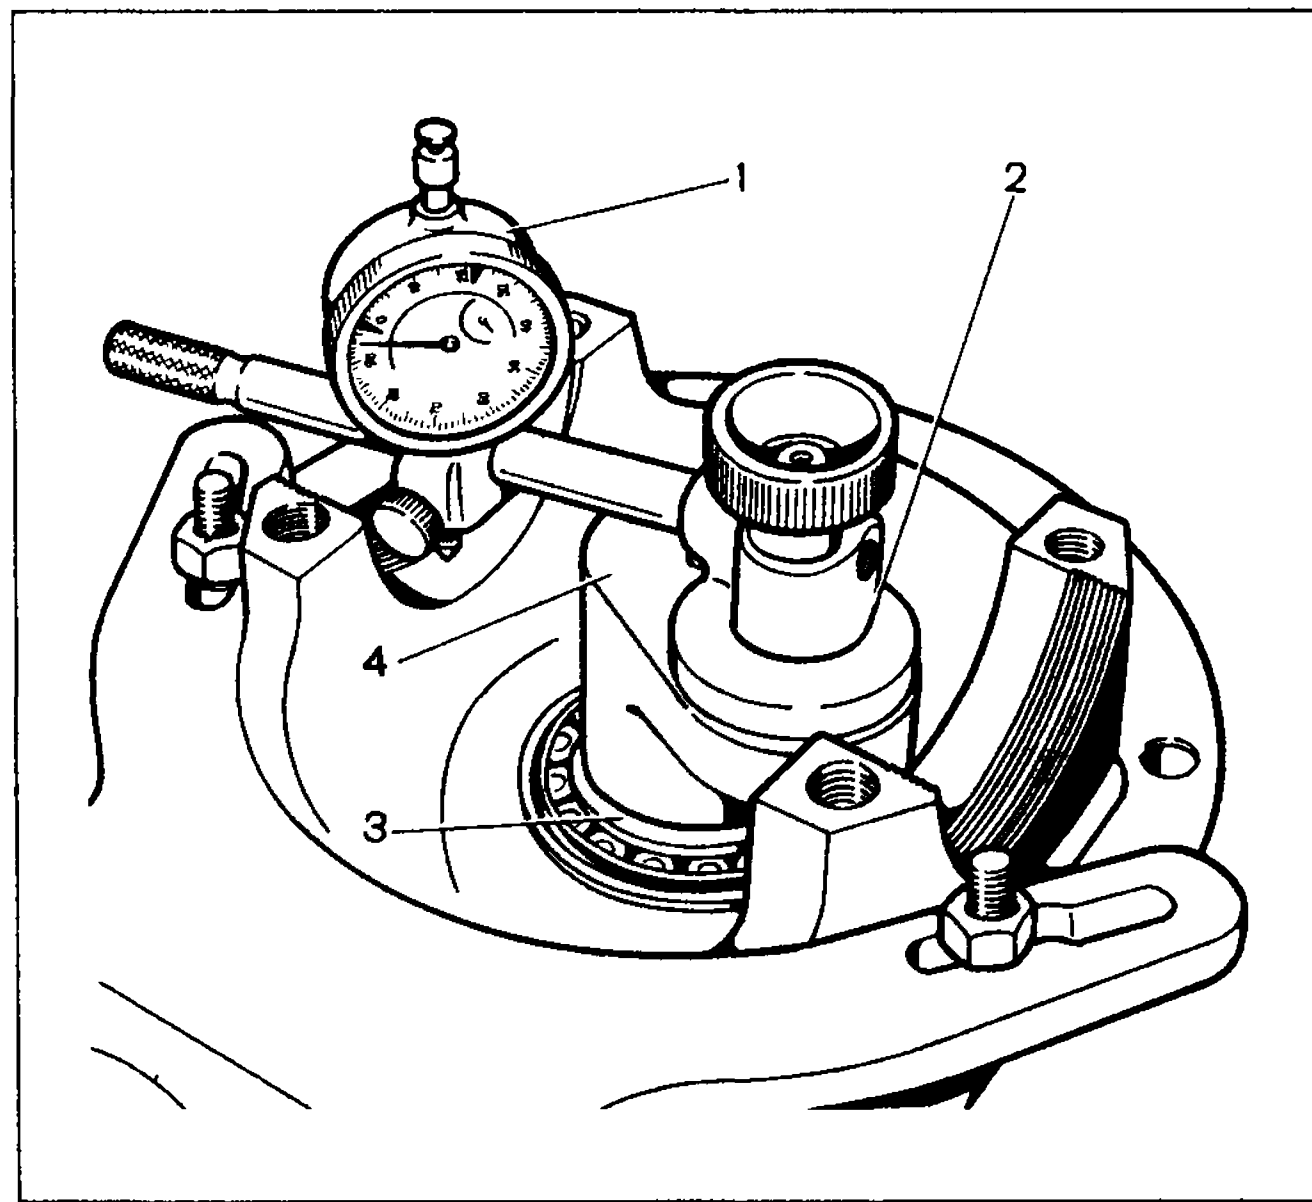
Определение толщины регулировочного кольца ведущей шестерни:
